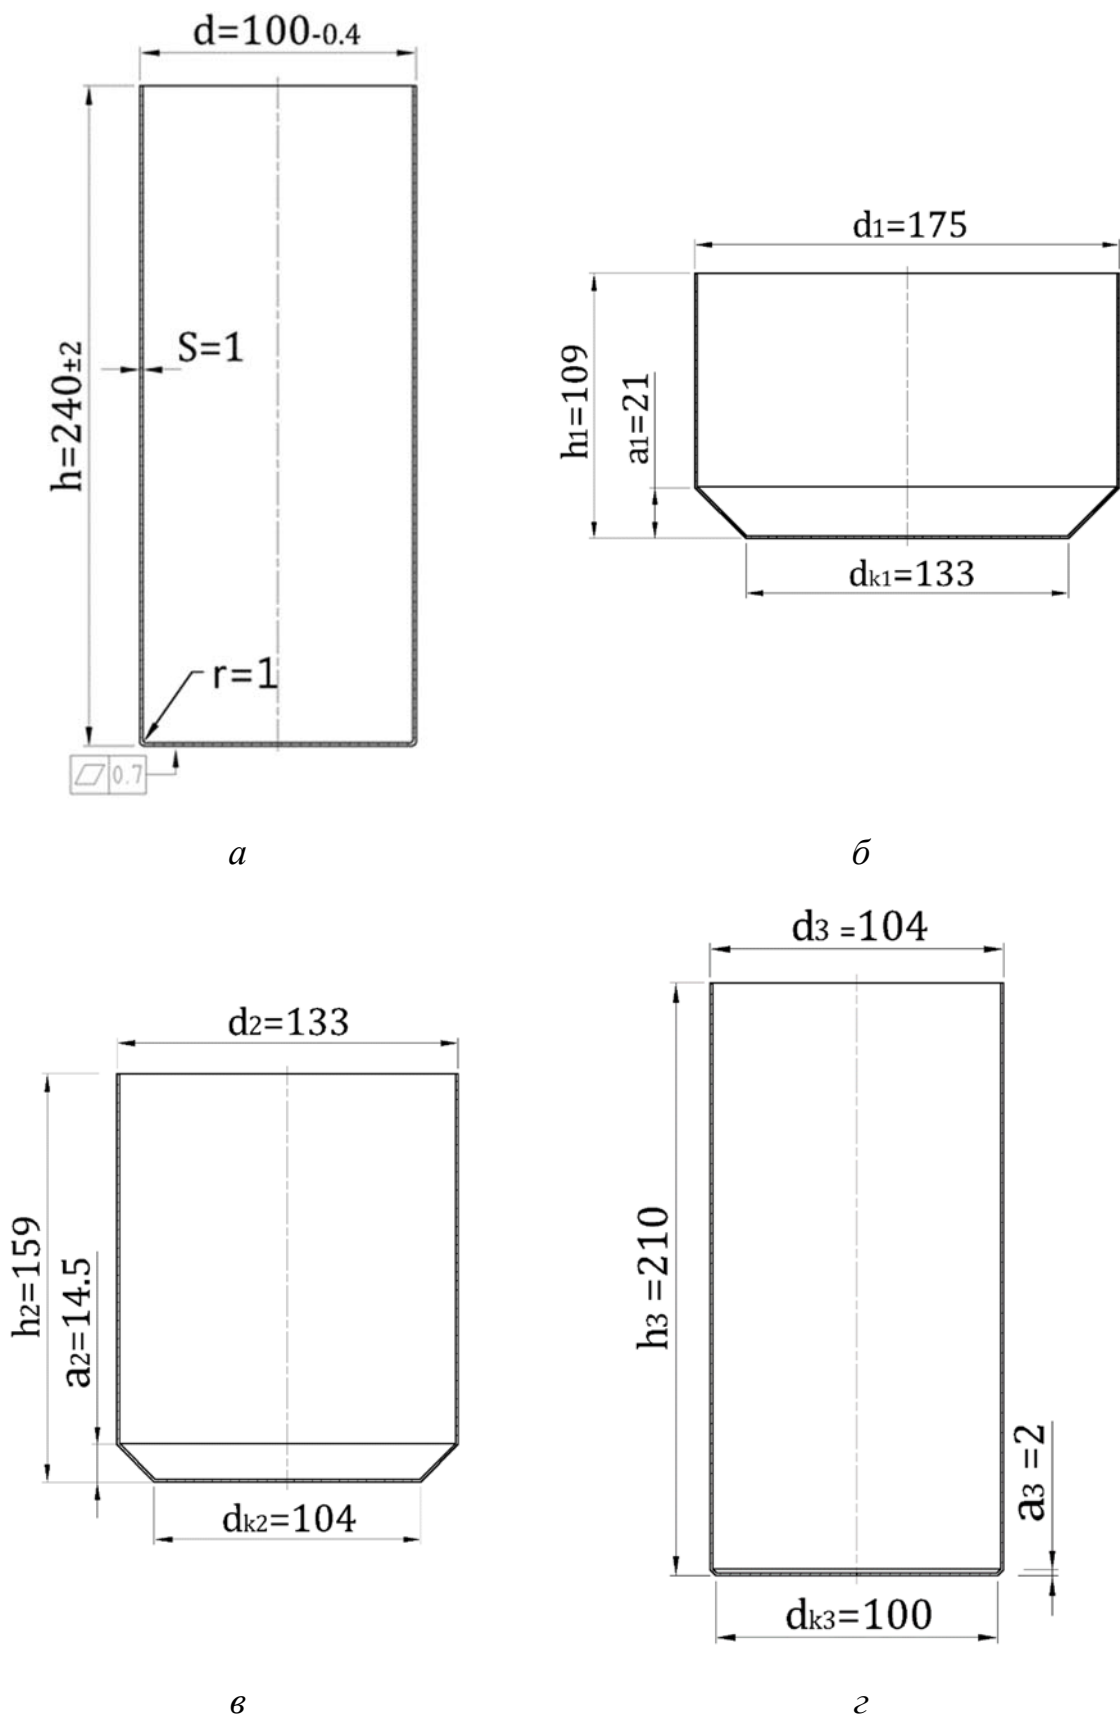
Креслення деталі (а) і схеми переходів витягання (б-г)
